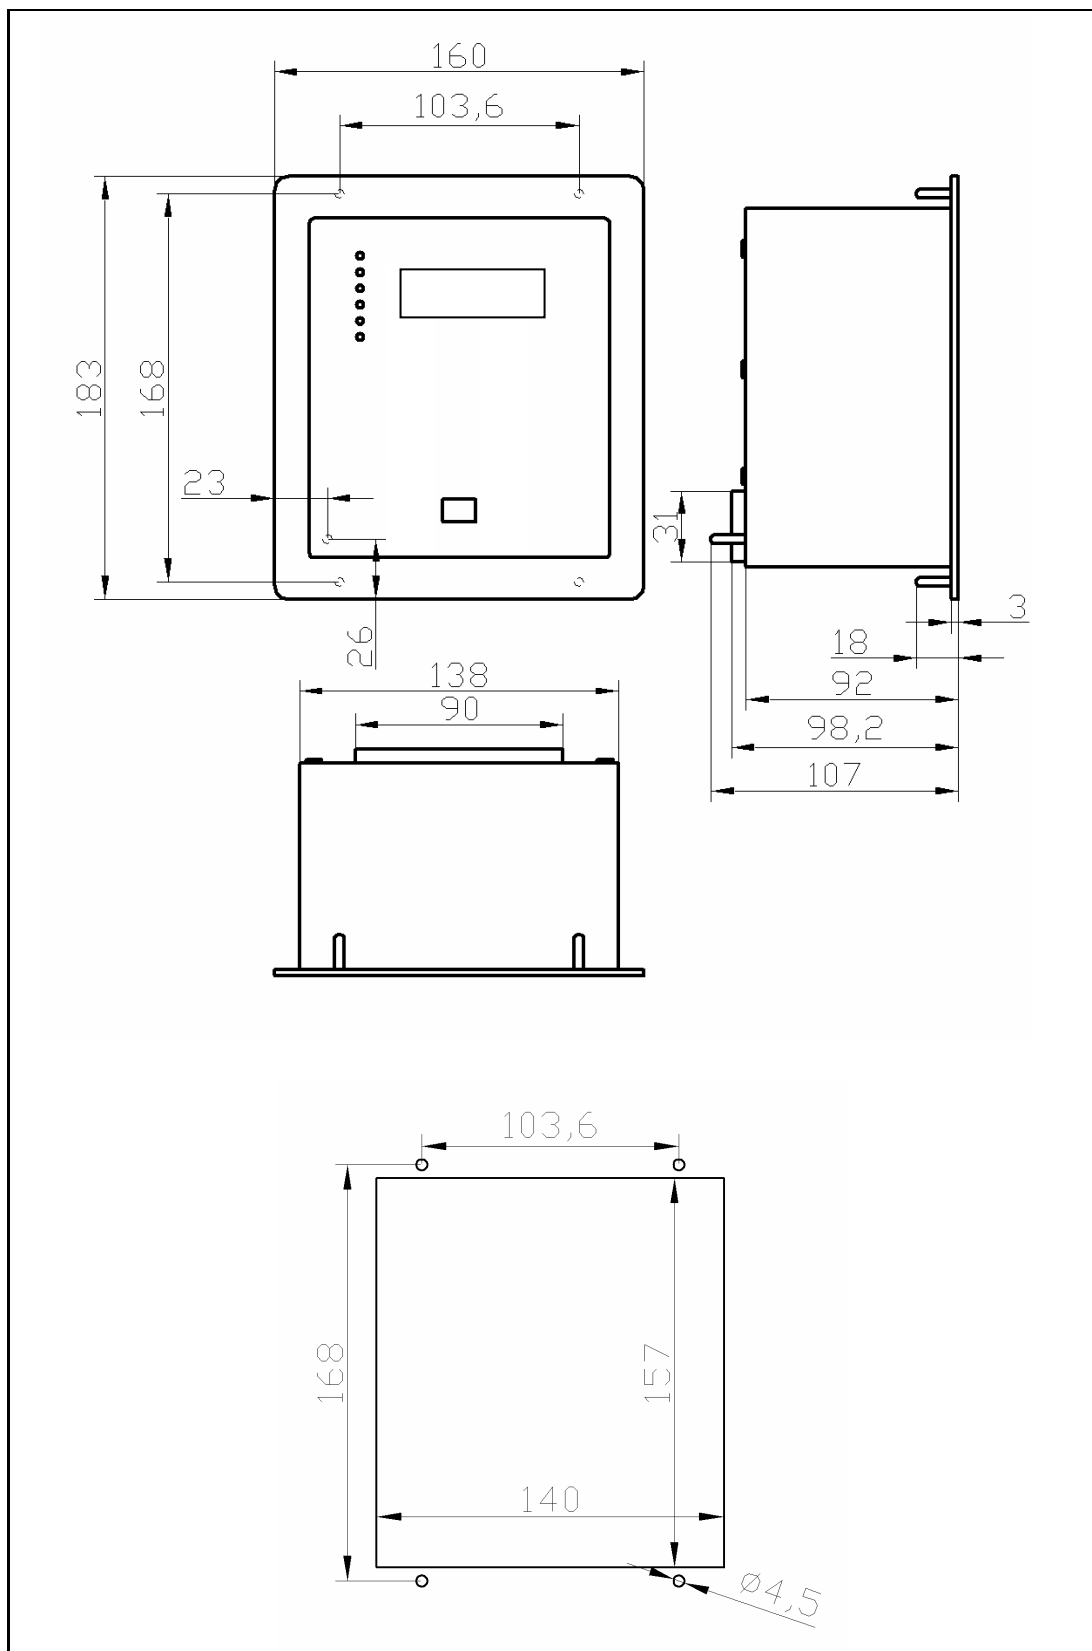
Размеры. Корпус P115 для монтажа "заподлицо"
